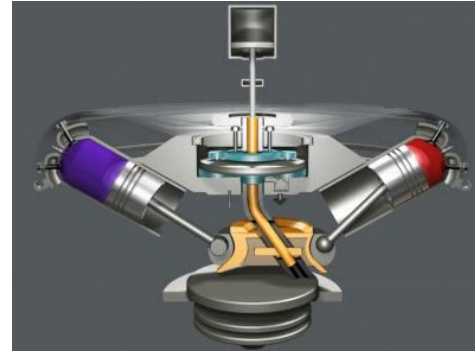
Doorsnede cillinder Alvar-cycle motor [33].
